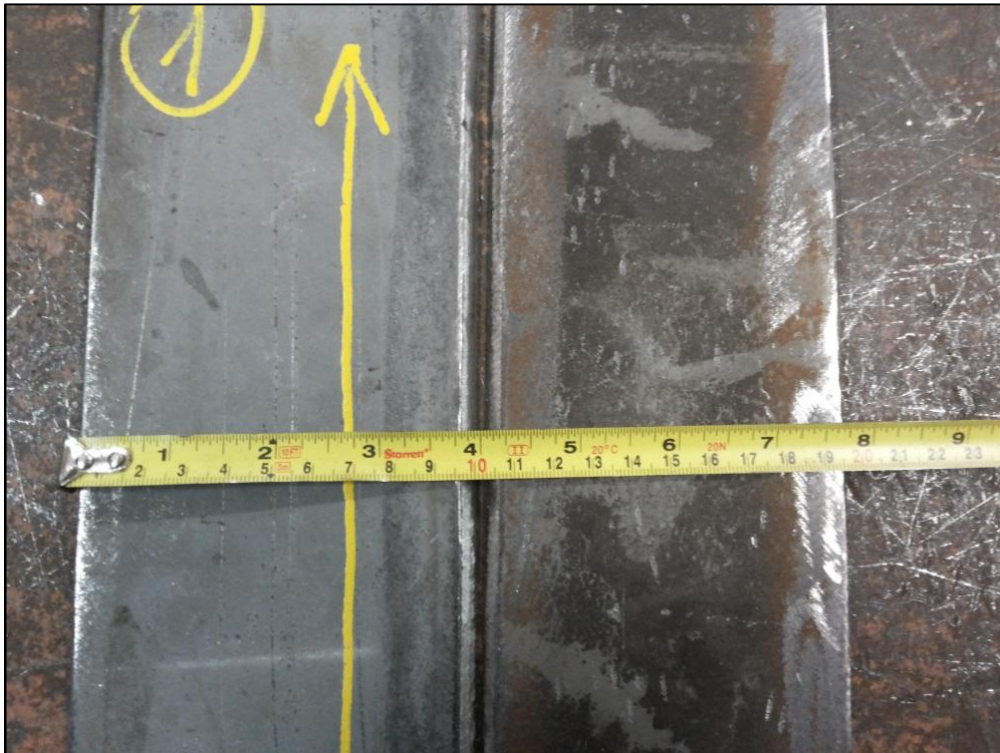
Dimensões dos corpos-de-prova-largura de 200 mm.
